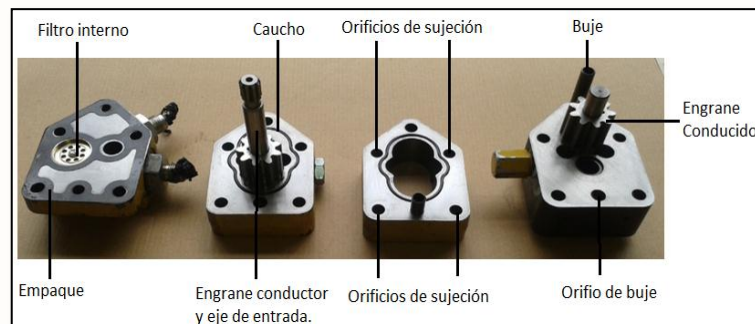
10: Despiece de la bomba de transferencia de combustible.
